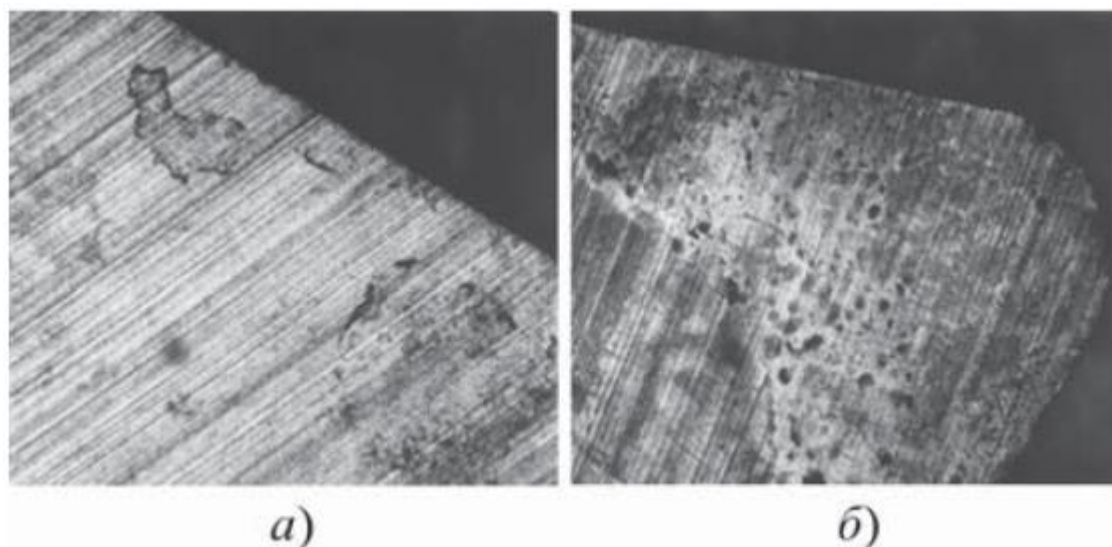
Загрязненные поверхности режущих пластин:
